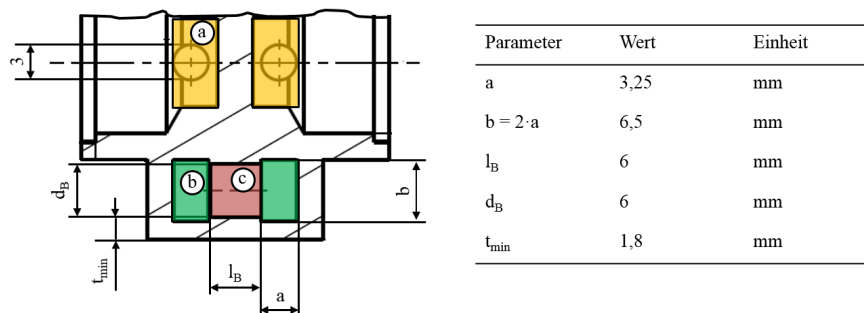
Detaillierte Geometrie des Kühlkanals: a) Zuleitungsbohrung, b) Kühlkanal und c) Verbindungsbohrung.
